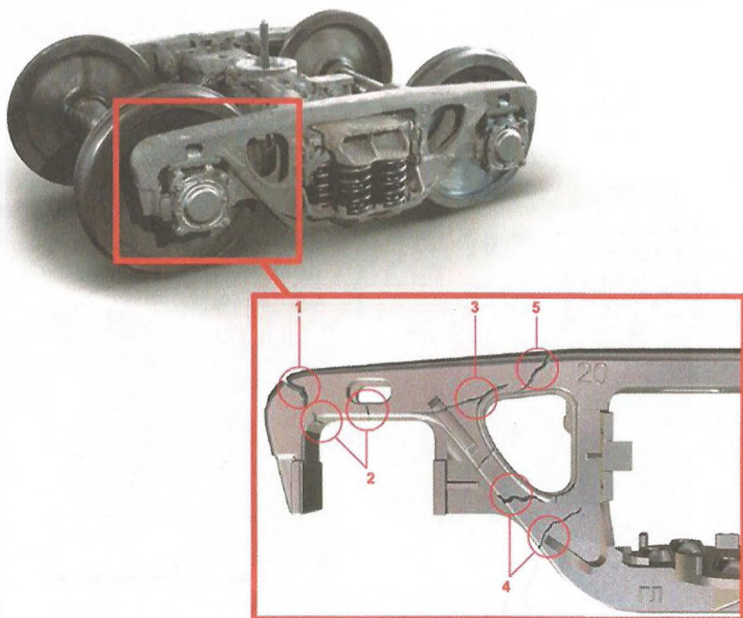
Трещина в литой боковой раме, надрессорной балке литой конструкции (вырубки пороков стального литья, произведенные после изготовления и ремонта надрессорных балок, не служат основанием для браковки)
